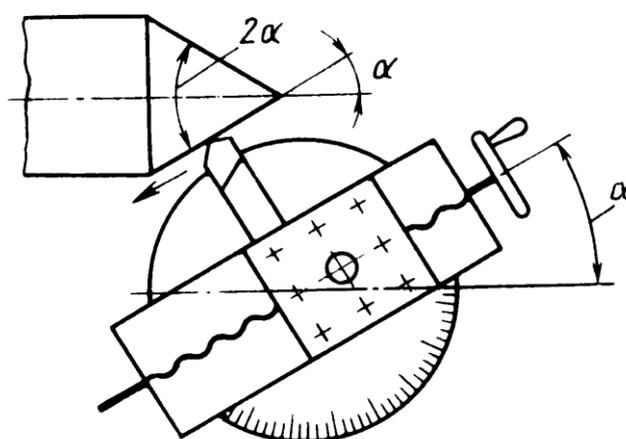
Схема точения конических поверхностей путём поворота верхних салазок суппорта
